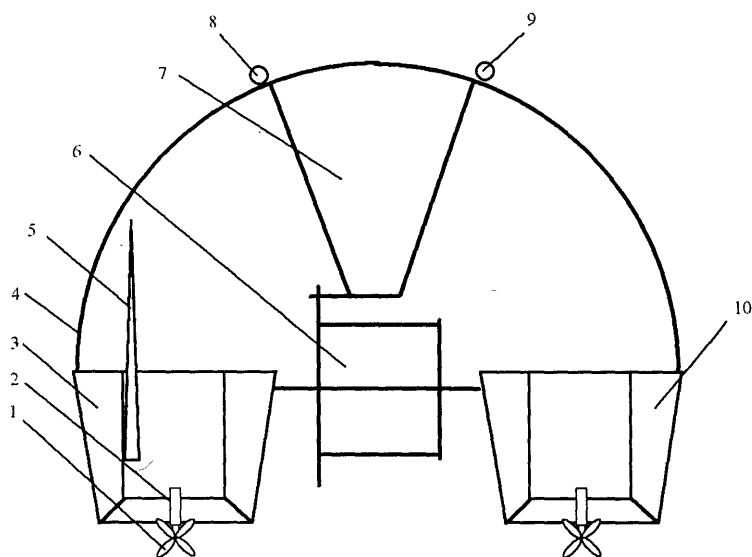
Вид со стороны кормы: 1 — винт; 2 — кожух вала винта; 3 — левый корпус катера; 4 — вертикальная стяжка; 5 — антенна; 6 — барабан прикормки; 7 — бункер; 8 — светодиод индикации работы приемника; 9 — светодиод индикации вращения барабана; 10 — правый корпус катера
